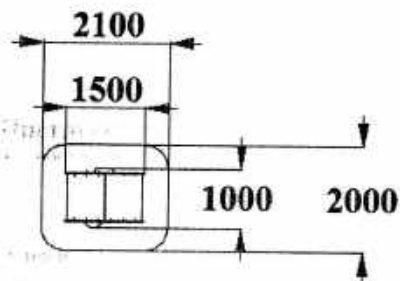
Габаритные размеры изделия. Размеры площадки для установки.
